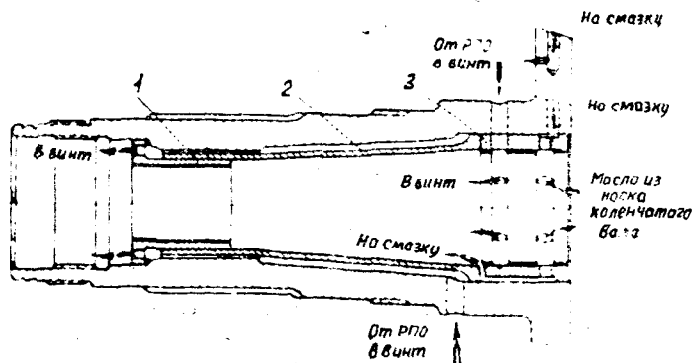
Продольный разрез вала винта: 1—передняя втулка; 2—гильза; 3—втулка задняя
